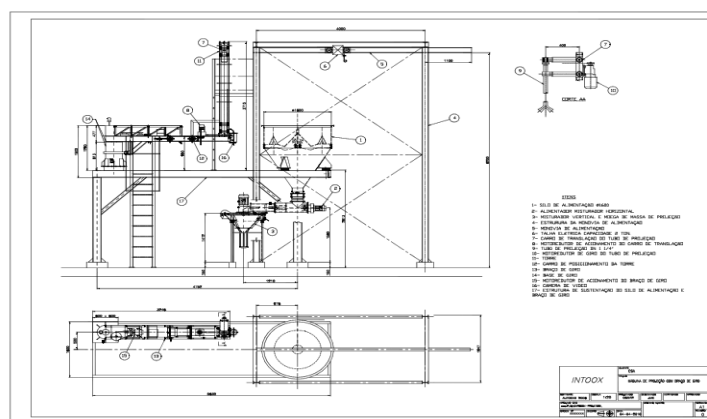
Desenho esquemático da instalação de aplicação automática.
